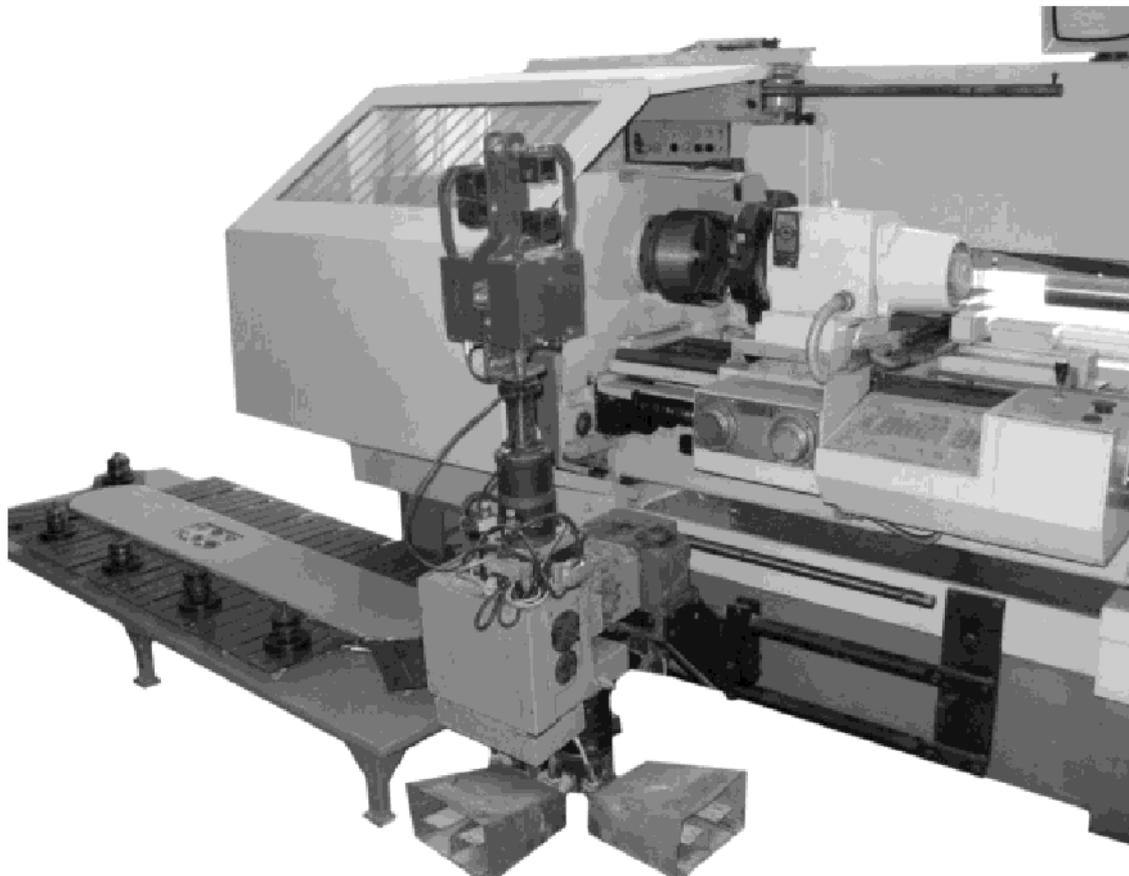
АРМ на базі токарного верстату 16К20Ф3
